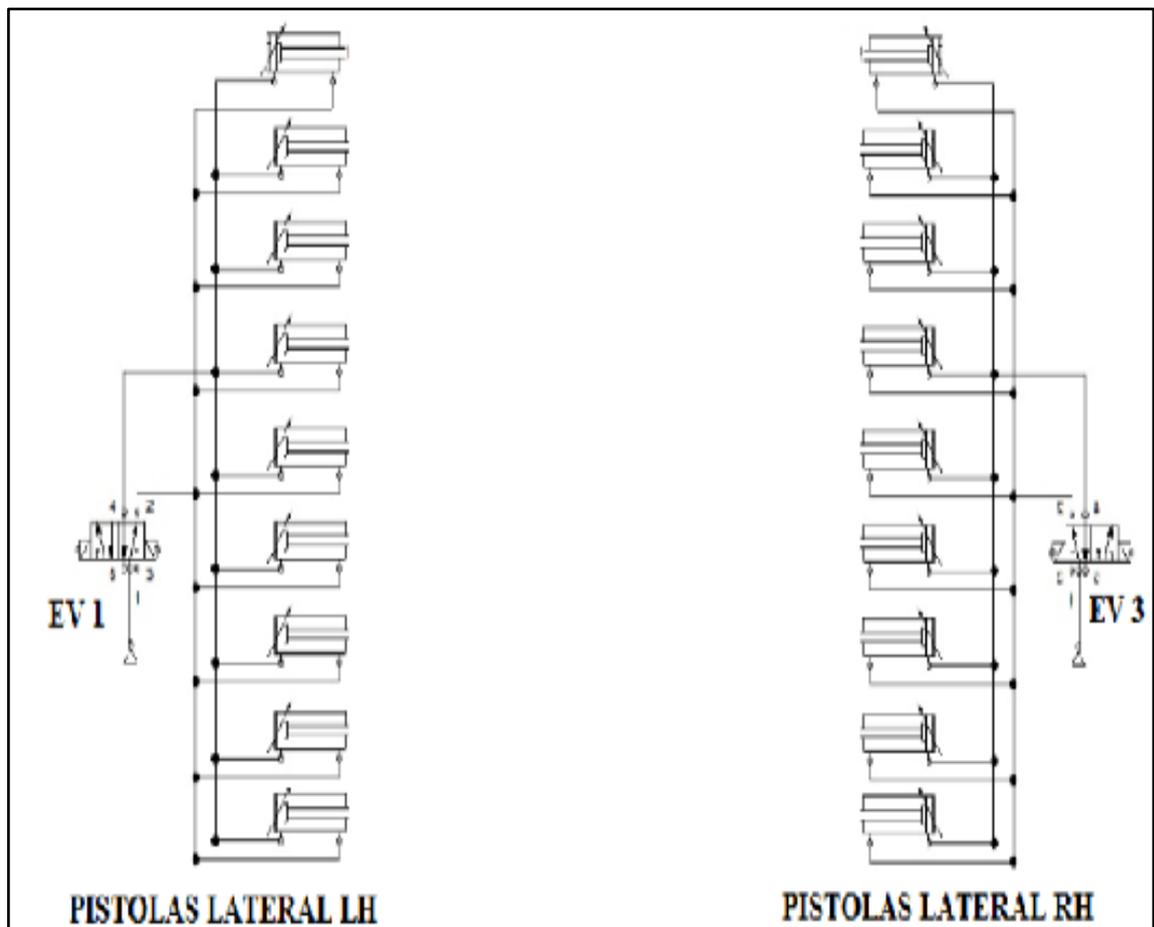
Esquema sistema electro neumático de soldadura inicial
